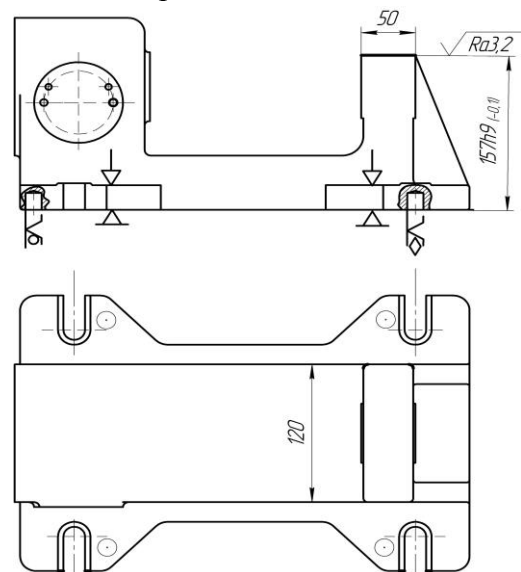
Схема обробки площини корпусної деталі в розмір 157h9
